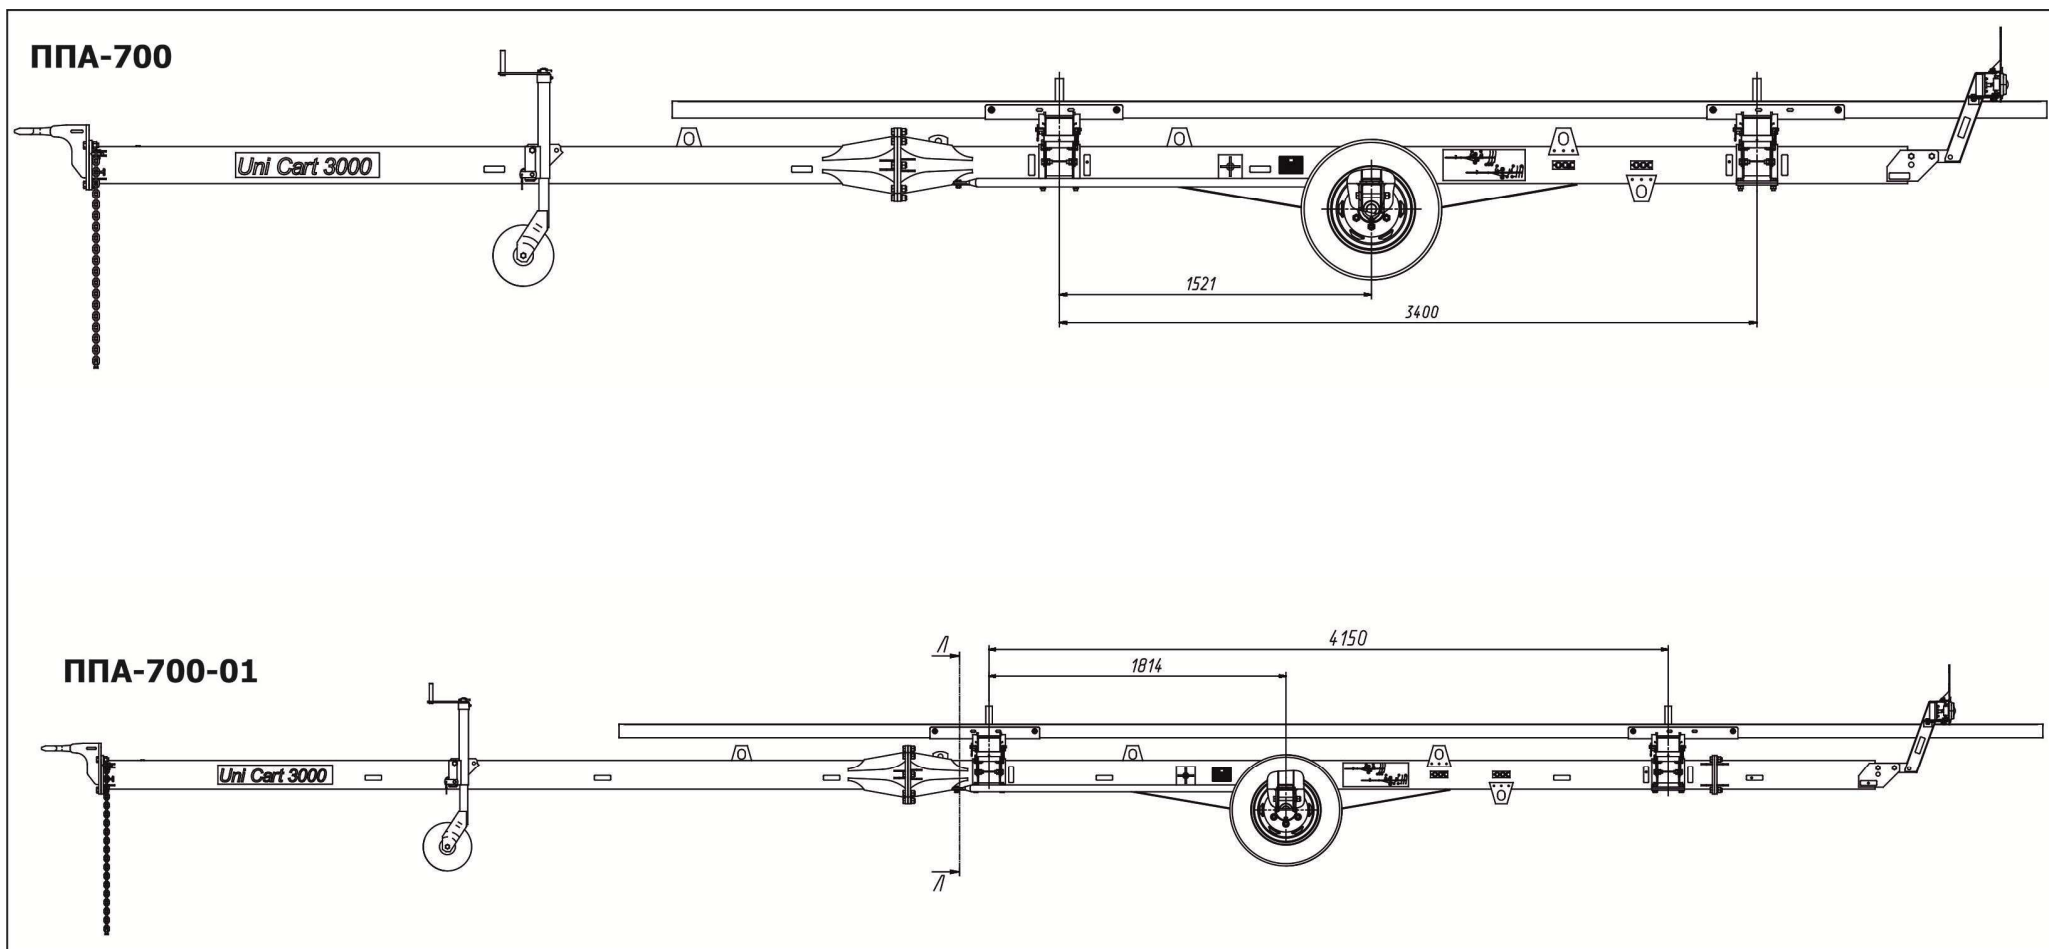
Схема установка опор на приспособления ППА-700 и ППА-700-01
